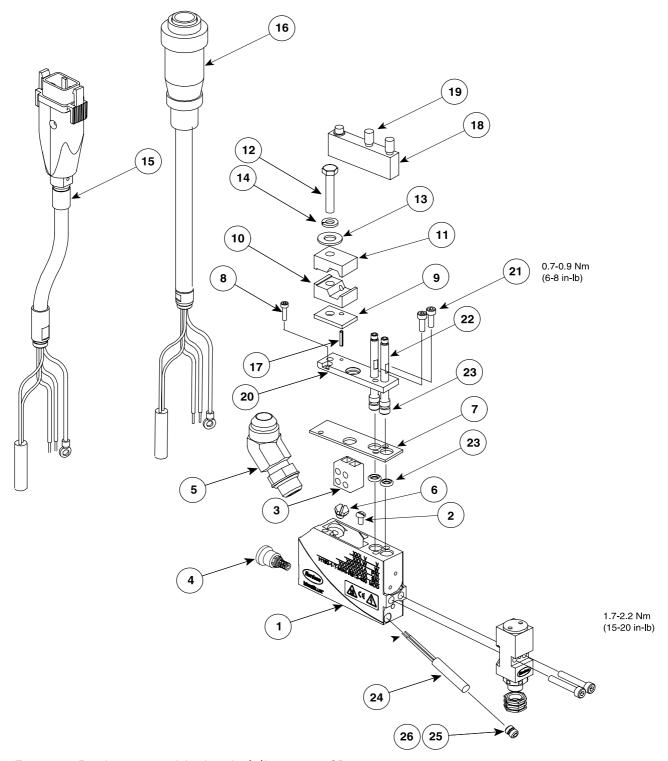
Pistolet mono-module ultra-plat à électrovanne SD
